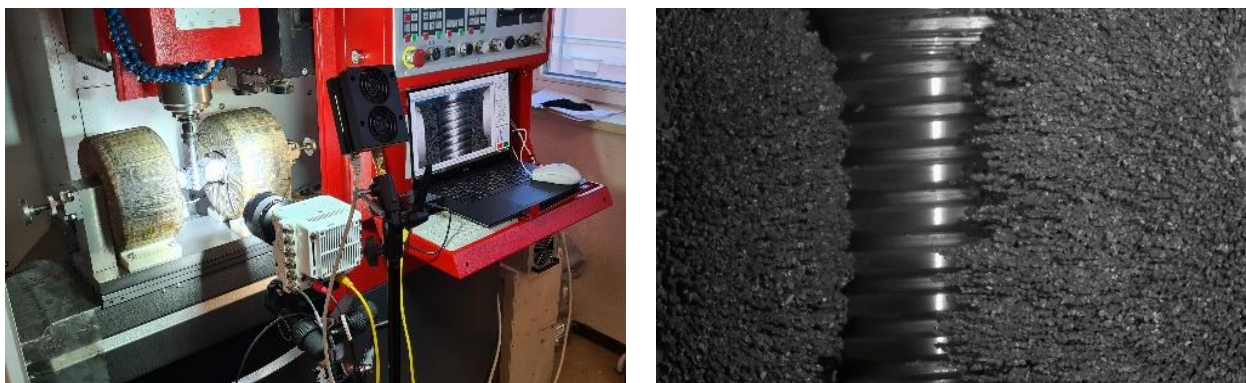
Процесс магнитно-абразивной обработки наружной резьбовой поверхности буровой штанги.
